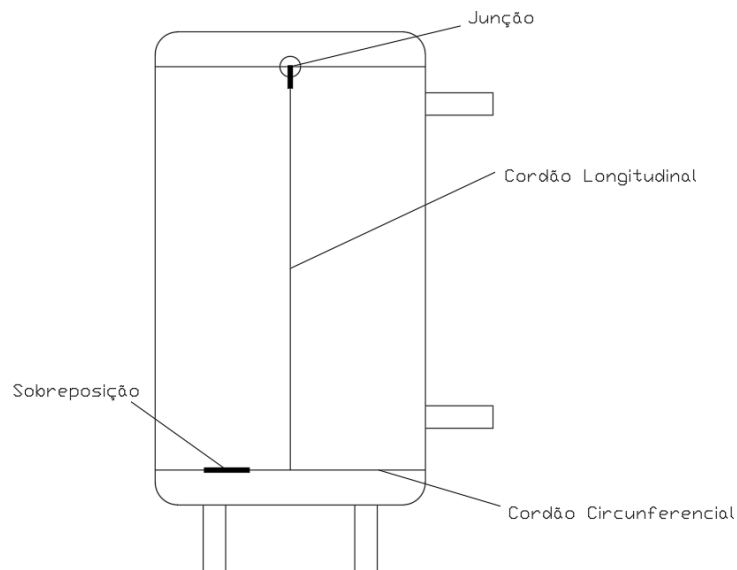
Juntas Críticas da Soldadura de Reservatórios
